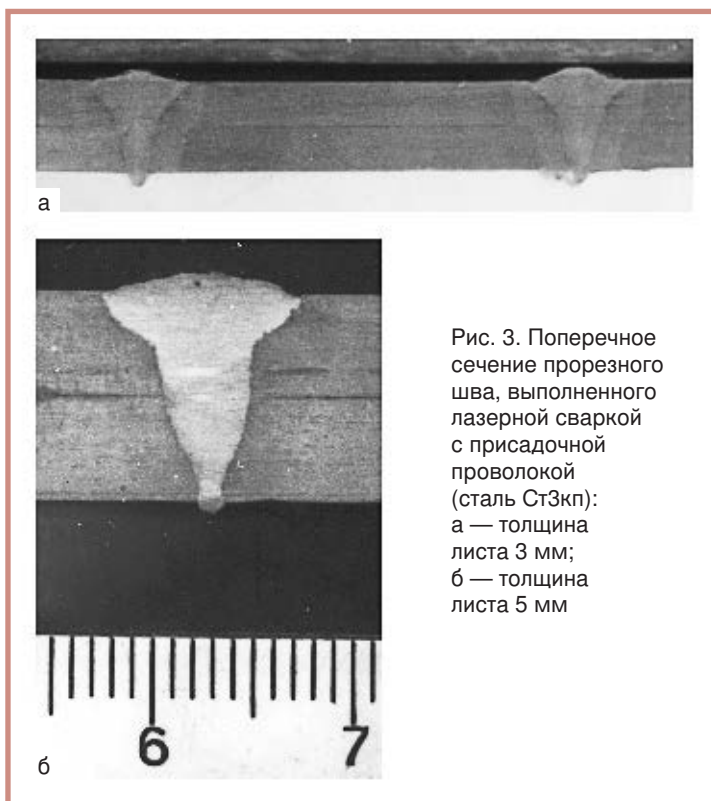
Поперечное сечение прорезного шва, выполненного лазерной сваркой с присадочной проволокой (сталь Ст3кп): а — толщина листа 3 мм; б — толщина листа 5 мм
